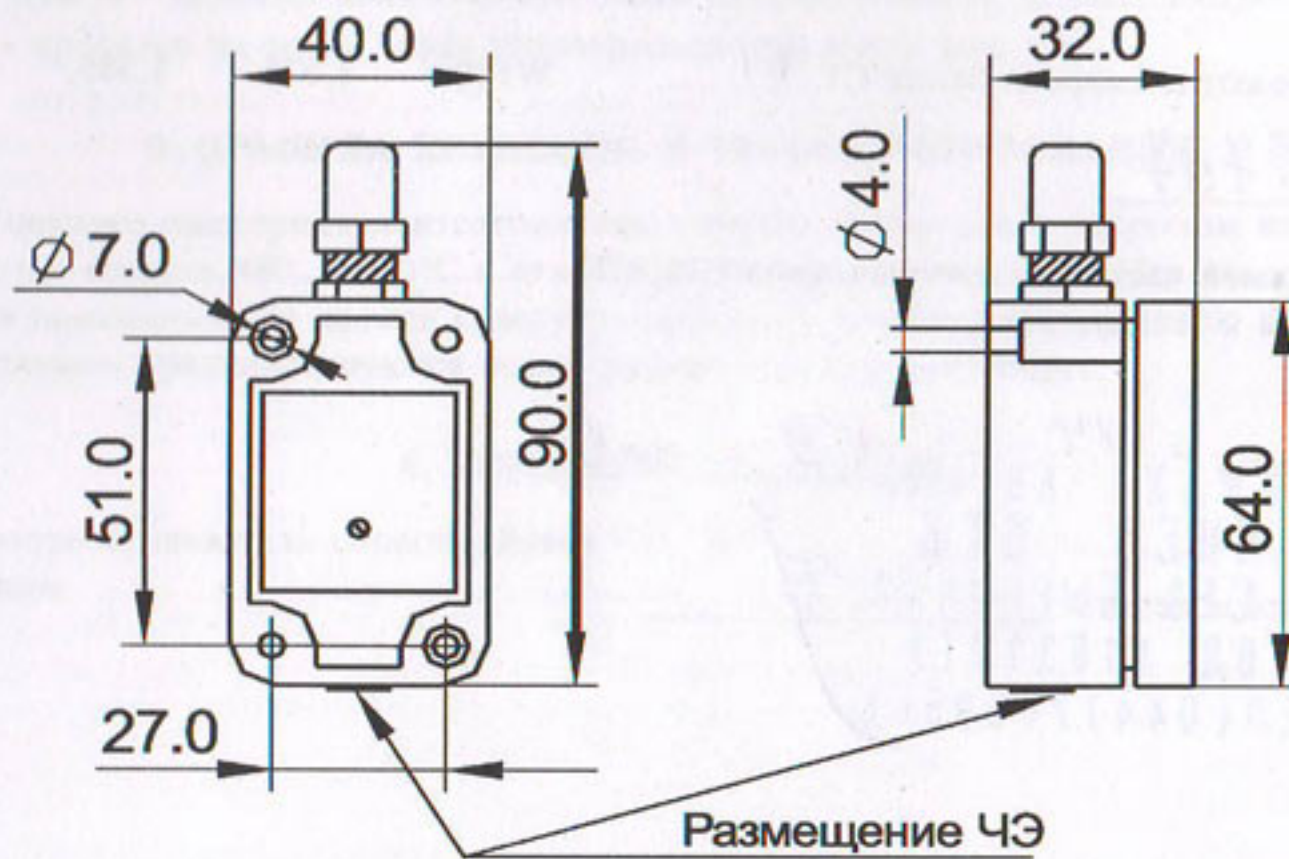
Конструктивные особенности и габаритно-присоединительные размеры датчика СТ-01
